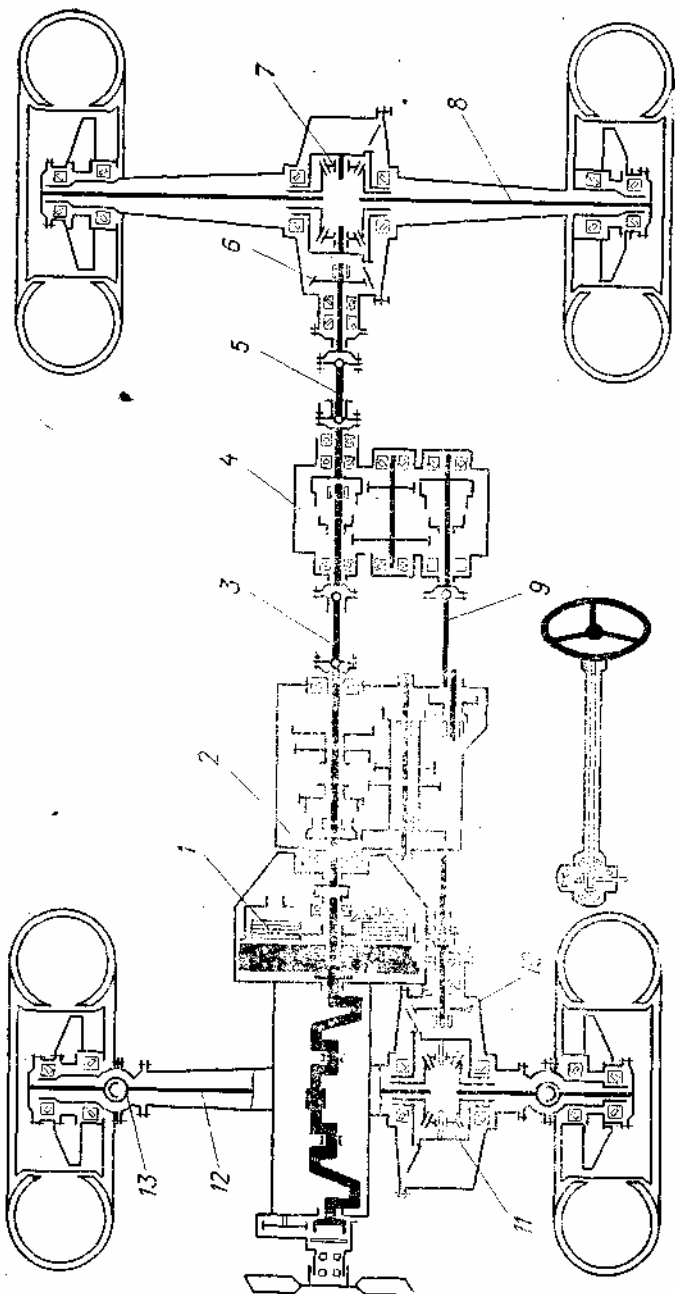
Схема силовой передачи автомобиля ГАЗ-66 с двумя ведущими осями
